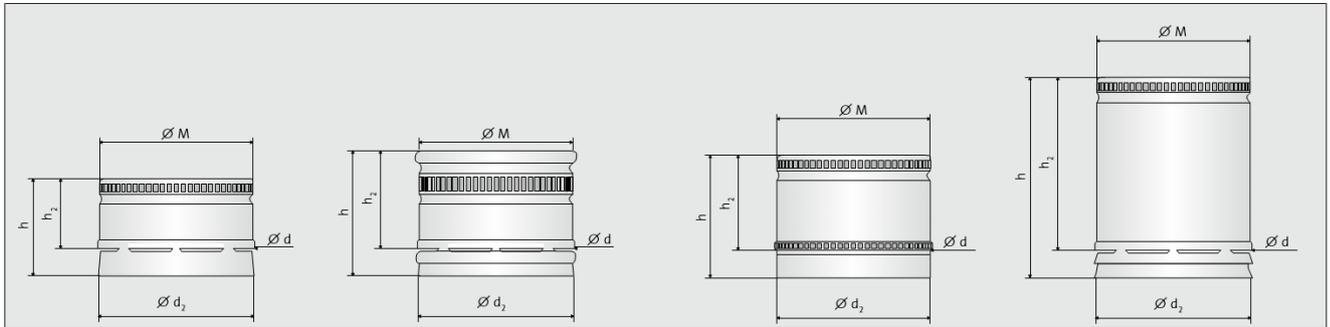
Technische Zeichnungen von Aluminiumverschlüssen
